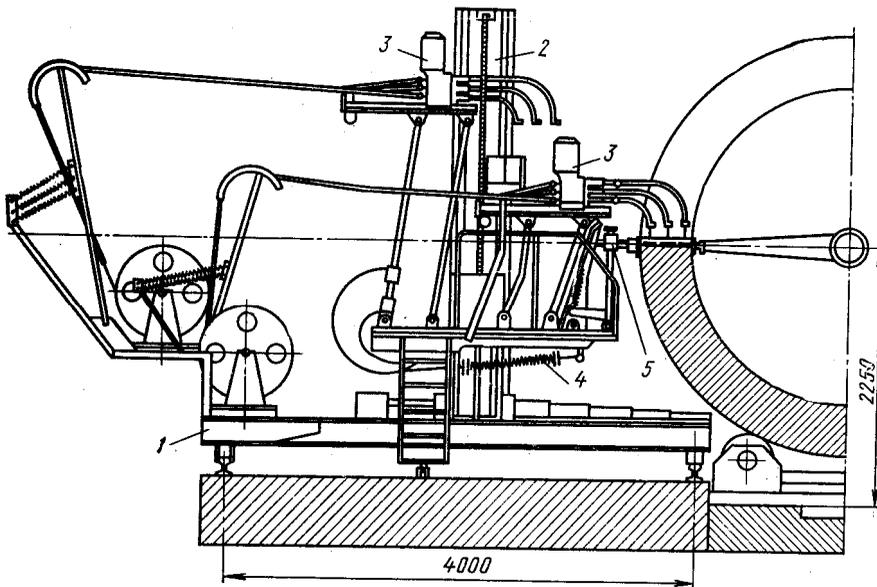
Установка с дублирующими головками для электрошлаковой сварки кольцевых швов:
